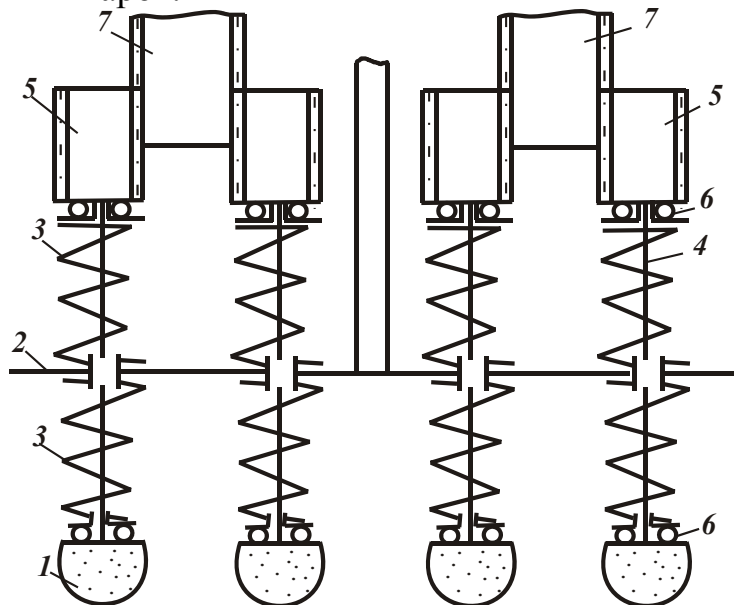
Шлифовальный инструмент для обработки фасонных поверхностей: 1 – шлифовальный шар; 2 – несущая плита – корпус; 3 – пружины; 4 – жесткий вал; 5 – подвижные шестерни-валы; 6 – подшипники; 7 – приводные шестеренчатые валы.
